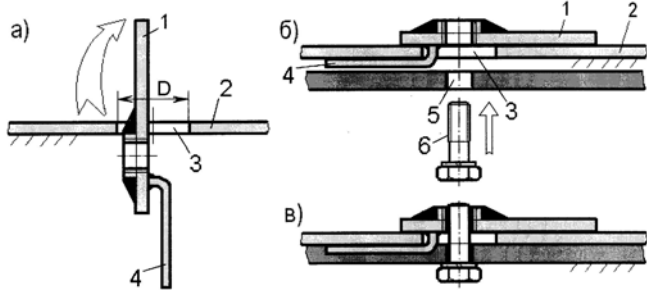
Последовательность крепления защитного поддона (а — установка монтажной планки в отверстие на силовом элементе моторного отсека; б — установка поддона и ввод болта в резьбовое отверстие планки; в — сборка болтового соединения): 1 — первая пластина; 2 — элемент конструкции автомобиля; 3 — отверстие в этом элементе; 4 — вторая планка; 5 — отверстие в защитном поддоне; 6 — болт крепления поддона
